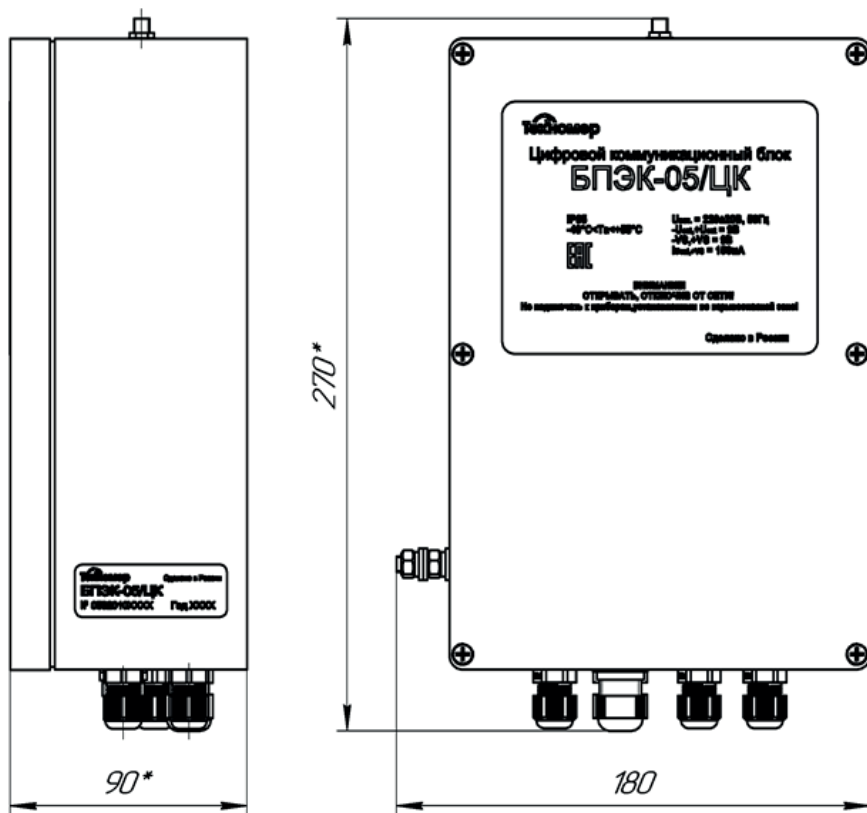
Габаритные размеры блока БПЭК-05/ЦК
